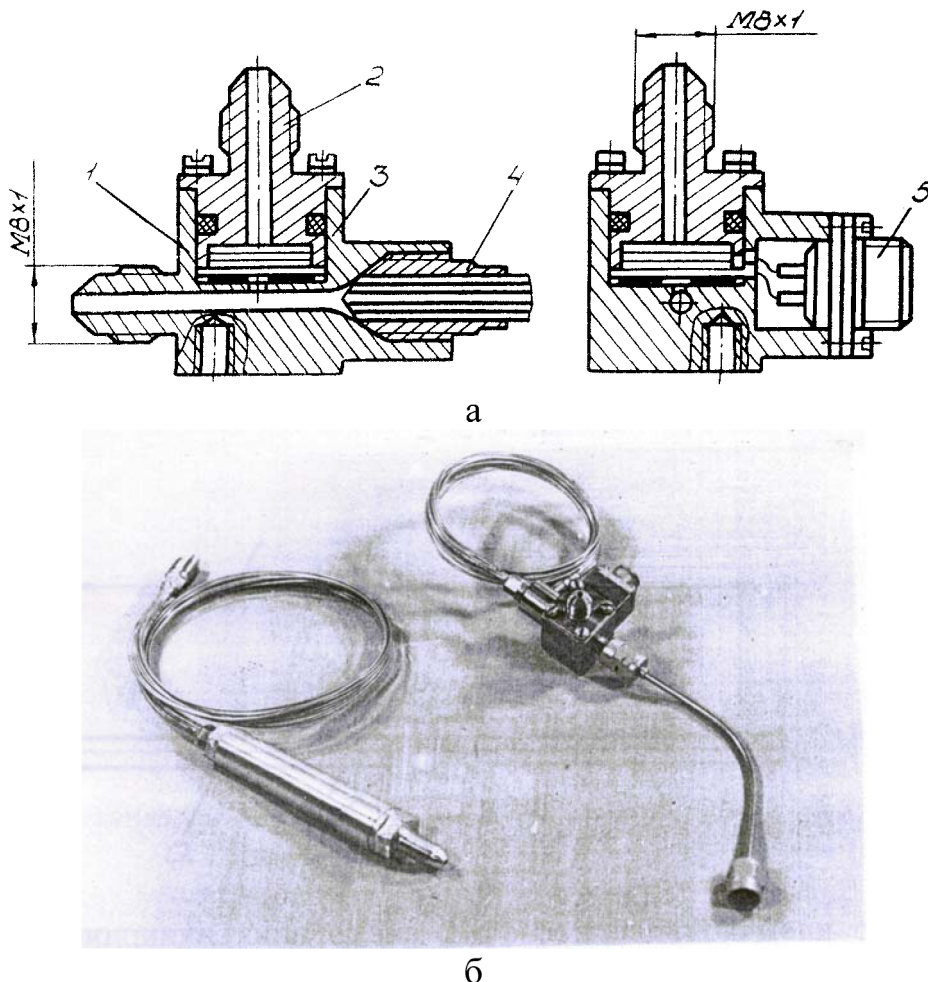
Конструктивная схема (а) и внешний вид (б) устройства для измерения динамического давления в узлах поршневого двигателя: 1 - датчик пульсации давления ДМИ-0,6-1; 2 - штуцер статической камеры; 3 - корпус устройства; 4 - пучок капиллярных каналов; 5 - штепсельный разъем РС-4
